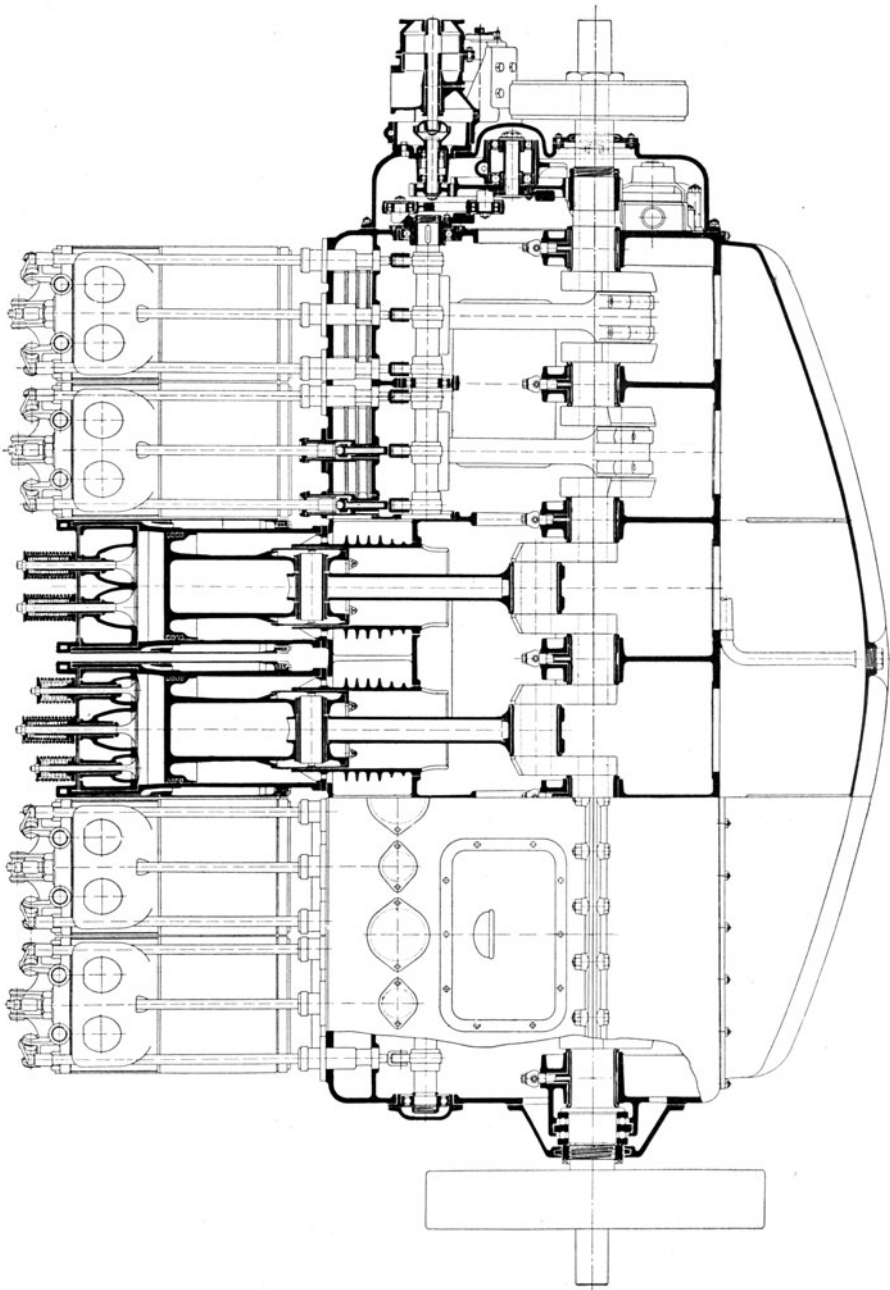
Längsschnitt einer Sechszylindermaschine nach Ricardo.
